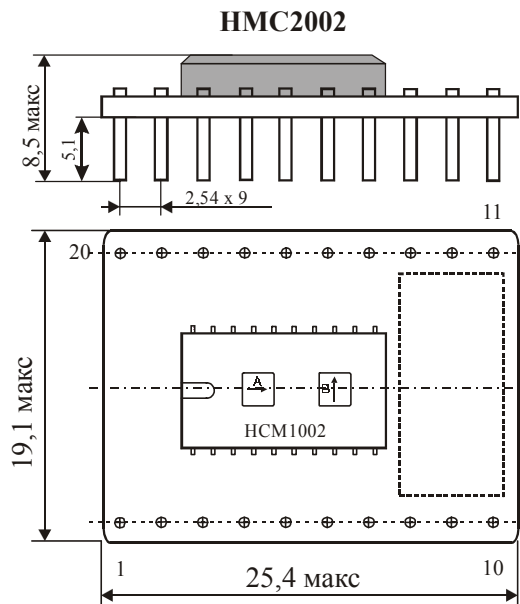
Внешний вид и габаритные размеры датчиков типа HMC 2002
